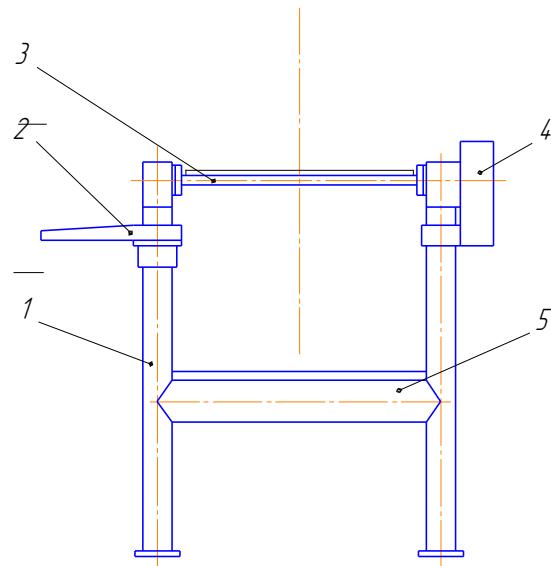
Стенд для разборки и сборки двигателей Р-236: 1 – рама; 2 – полка; 3 – поворотный стол; 4 – червячный редуктор; 5 – поддон.
